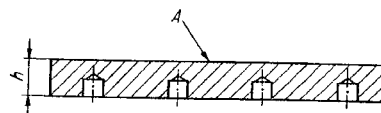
Планка 3, 4 уплотнительная /рис. 111/
